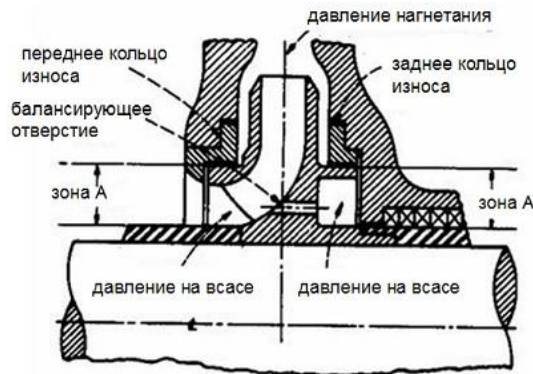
Рабочее колесо с балансировочными (разгрузочными) отверстиями
